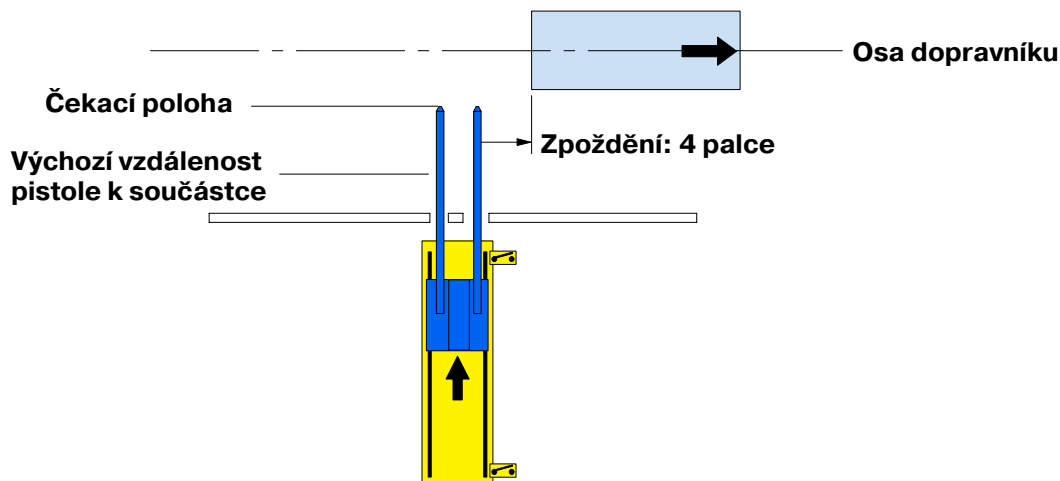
Součástka je před pistolemi: Vzdálenost pistole k součástce je udržována (pohled shora)
